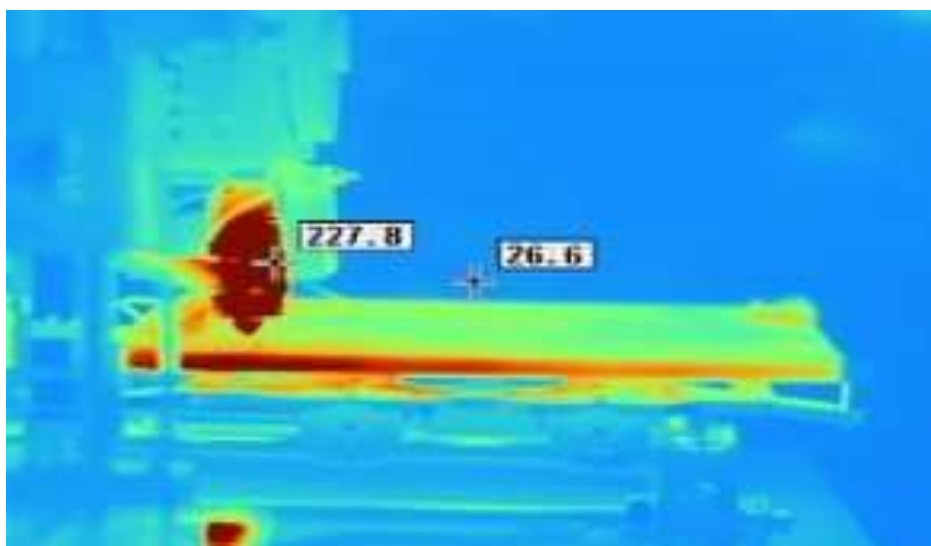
Zobrazení proudění vzduchu tiskovou hlavou.
